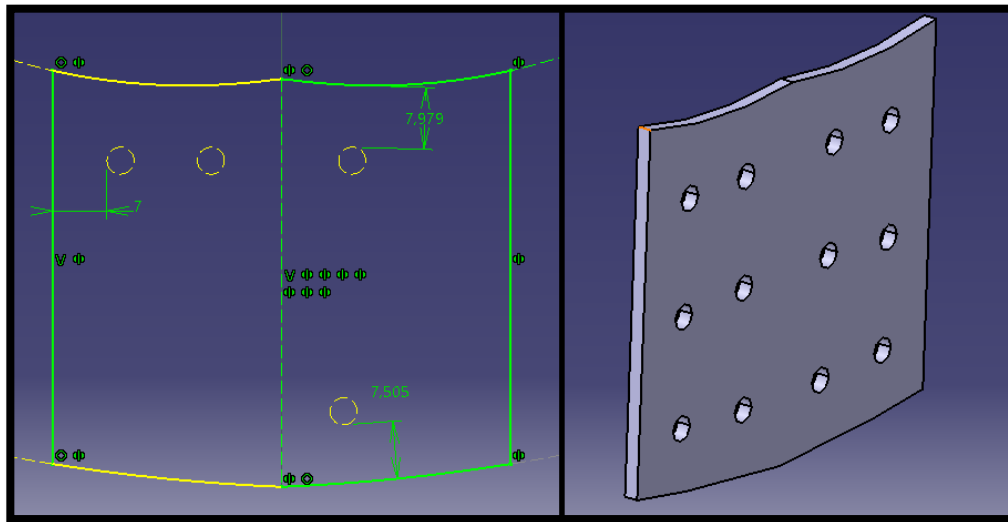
Refuerzo inferior 17: Sketch y pieza final tras extrusión y vaciado
